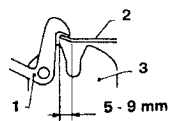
Регулировка положения предохранительной защелки - модели с кузовом типа "Универсал" и "Купе"
